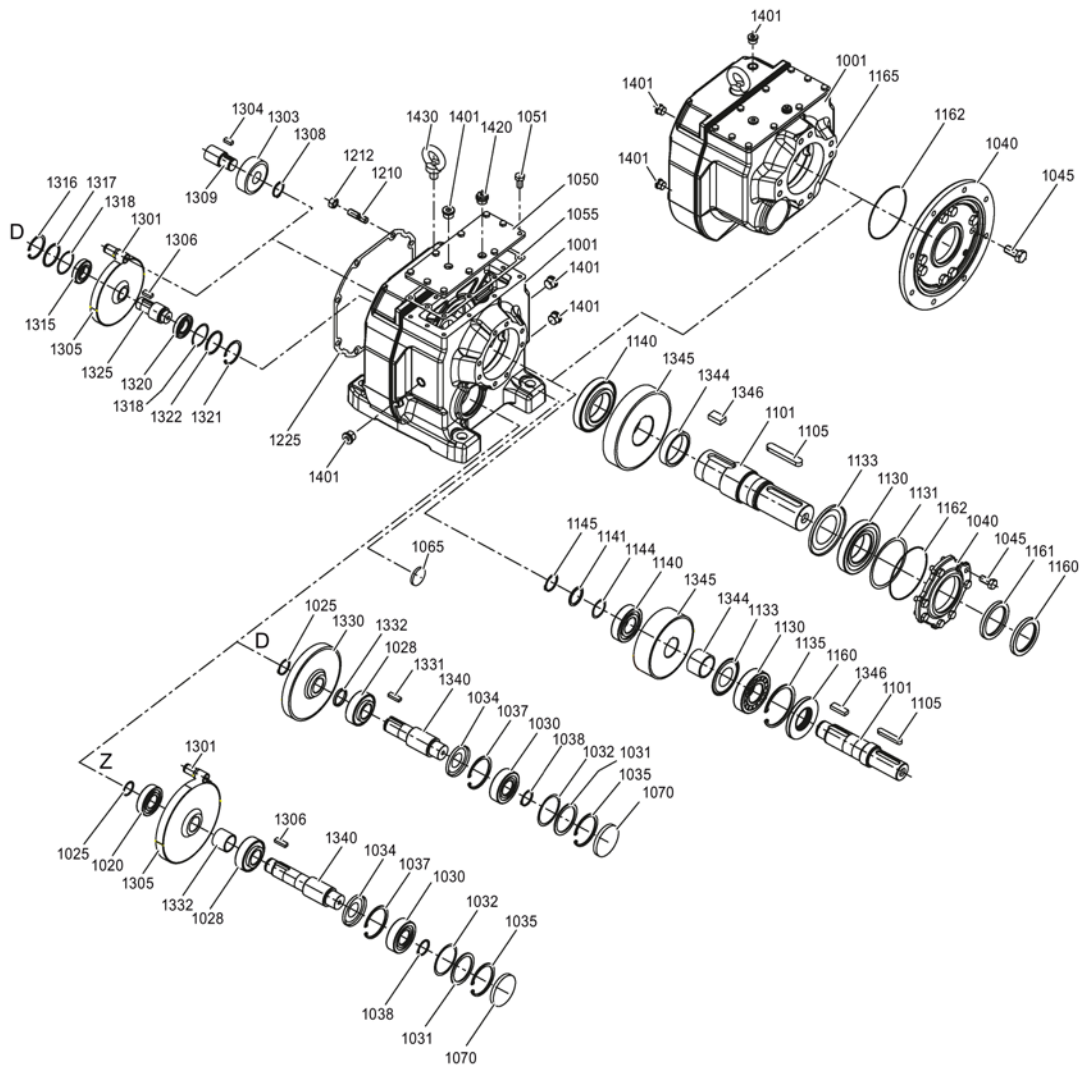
Przekładnia walcowa E wielkości 39 - 149
